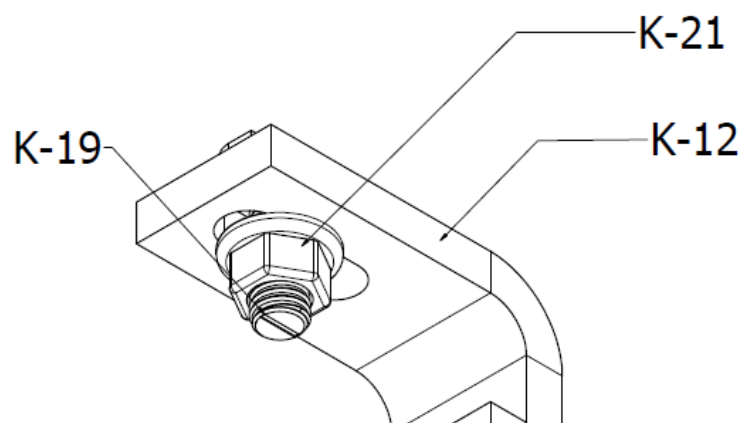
Pozycja śruby Teowej w kanale profilu po zablokowaniu
